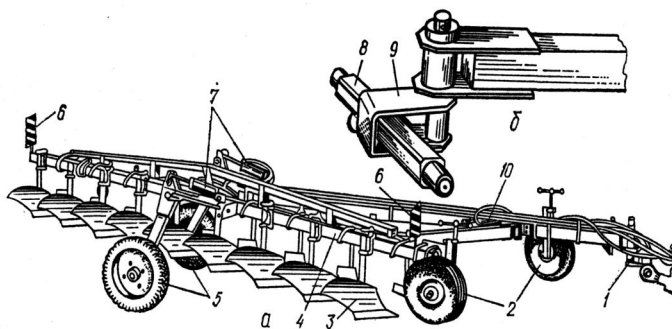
Напівначіпний дев'ятикорпусний плуг ПТК-9-35:
